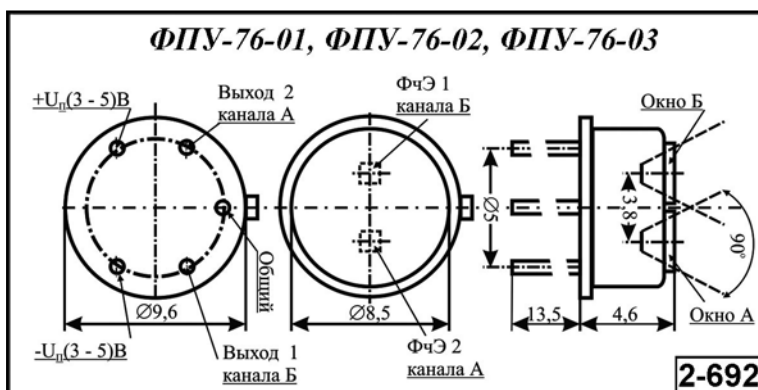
Внешний вид и габаритные размеры ФПУ-76
